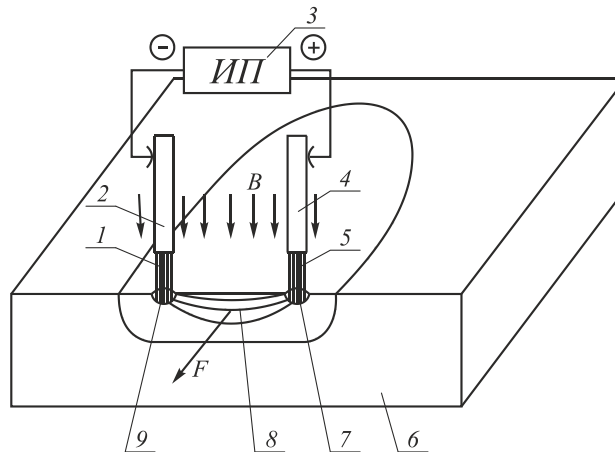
Схема разветвления линий тока в изделии при сварке двумя последовательно включенными дугами (обозначения в тексте)
